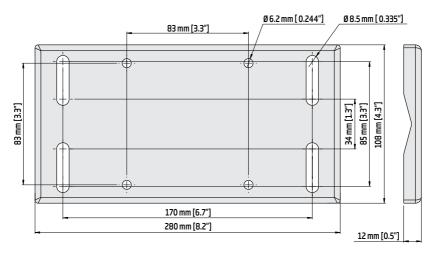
Espesor del panel para el montaje en la pared, pernos de montaje y dimensiones de las ranuras
